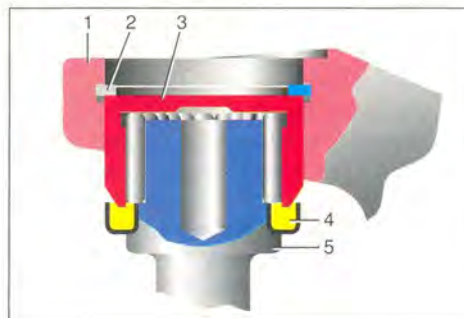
Подшипник крестовины карданного вала автомобилей ВАЗ-2101...-2107: 1 – проушина вилки; 2 – стопорное кольцо; 3 – подшипник; 4 – уплотнение; 5 – шип крестовины.
